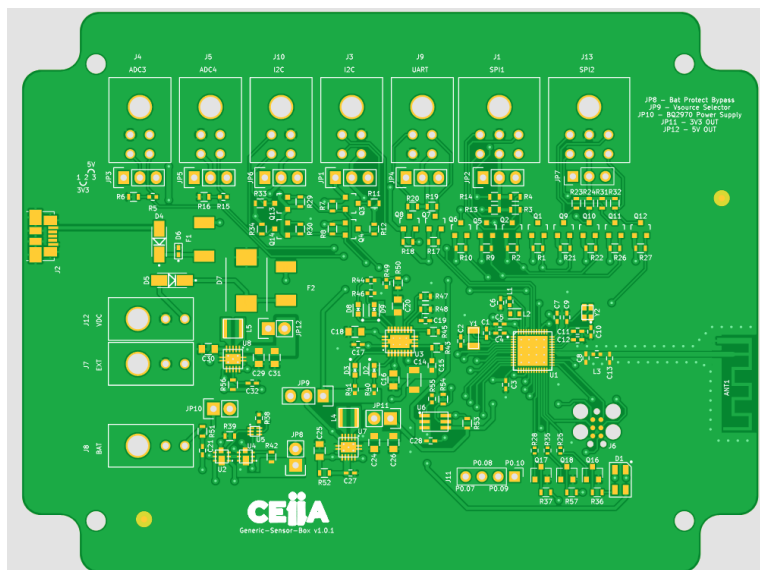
Desenho da PCB da Caixa de Sensores - Lado Superior
